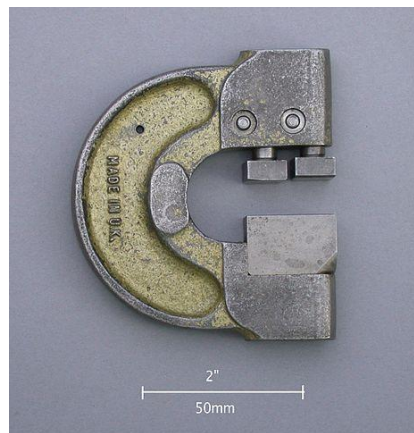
Вигляд калібру-скоби для контролю зовнішніх розмірів деталей [2]
